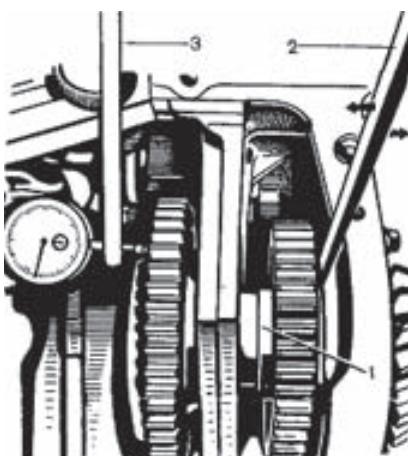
Проверка осевого зазора в подшипниках вторичного вала: 1 — вторичный вал; 2 — монтажная лопатка; 3 — индикатор.
